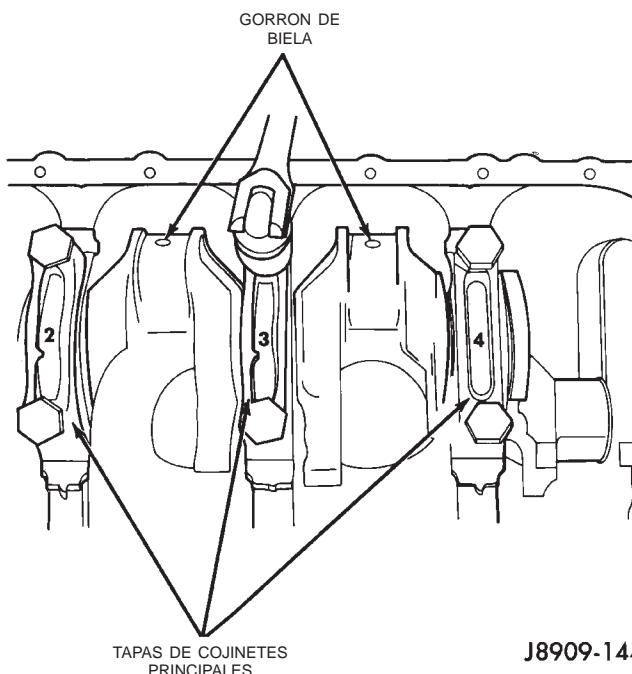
Desmontaje de tapas de cojinetes principales y encastres inferiores
